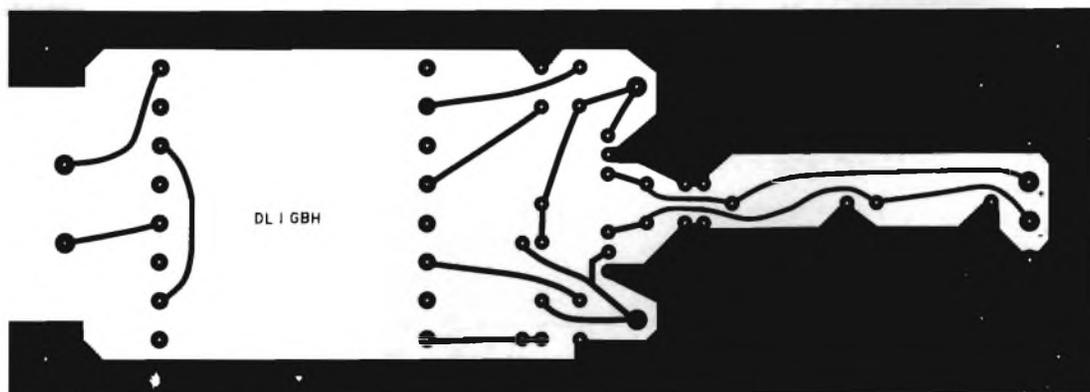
Piste di rame del circuito stampato dell'alimentatore, che può essere impiegato sia per l'alimentatore I che per l'alimentatore II.
